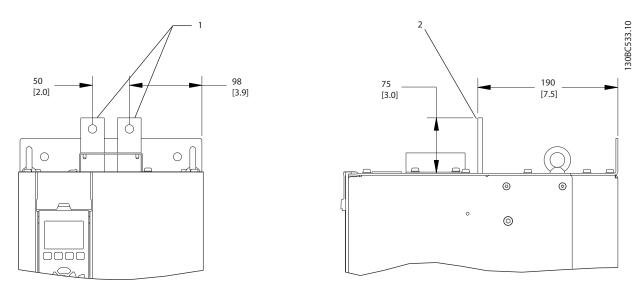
Terminais de regeneração e de distribuição da carga, D3h
